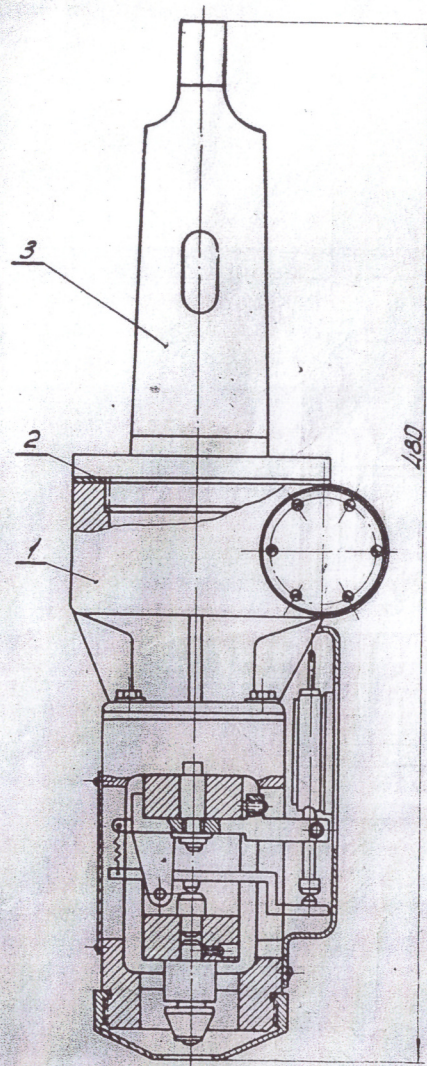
Приспособление для крепления прибора на вертикально-сверлильном станке:
